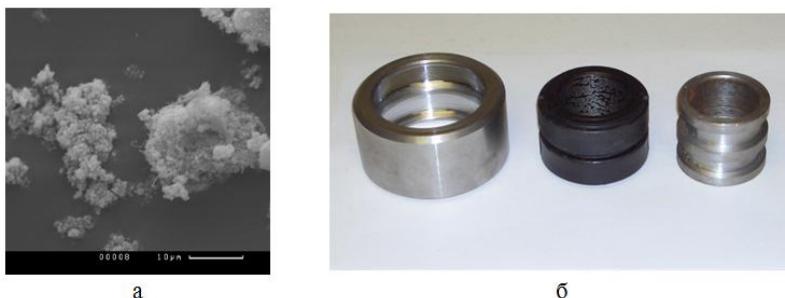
Внешний вид объектов: а — углеродный композит, полученный каталитическим пиролизом этанола при температуре 700 °С, давлении 20 кПа; б — детали подшипника скольжения поворотной опоры транспортера ТСН-160А (вкладыш изготовлен из ПНК, наполненного углеродными нанотрубками)
